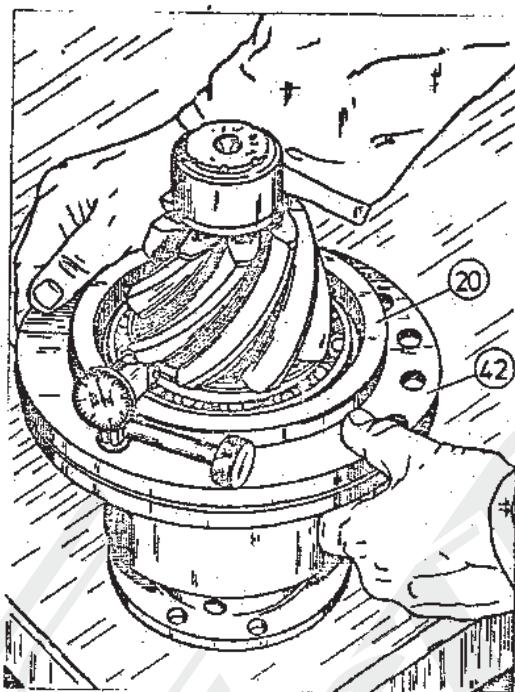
Измерение действительного размера от торцевой плоскости подшипника 20 до опорной плоскости корпуса узла приводного колеса 42.
